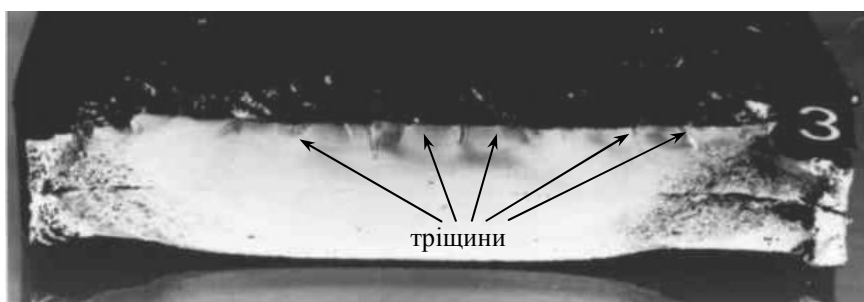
Поверхня руйнування зразка з привареною накладкою, що демонструє багатоосередковий характер зародження поверхневих тріщин
